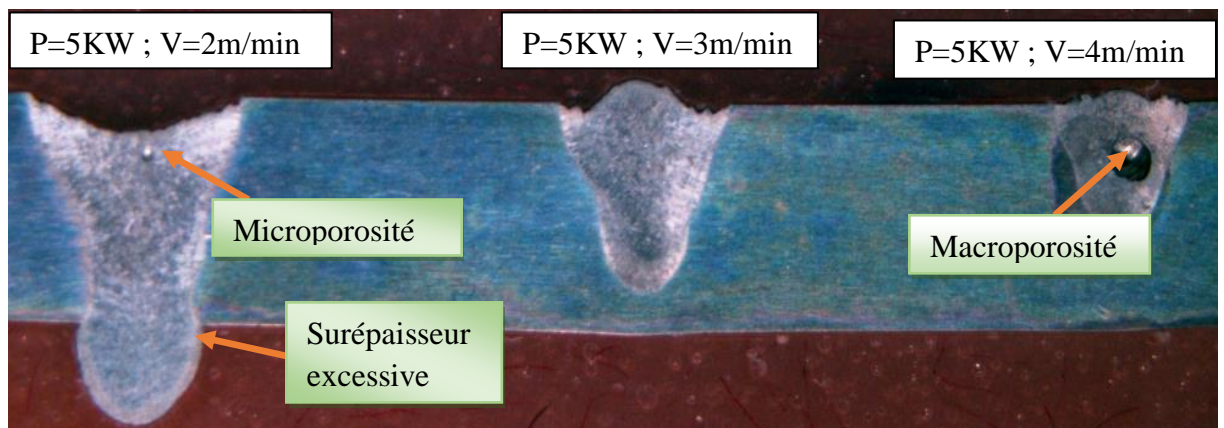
Macrographie des cordons pour un soudage à position focale -2mm(G6.7).
